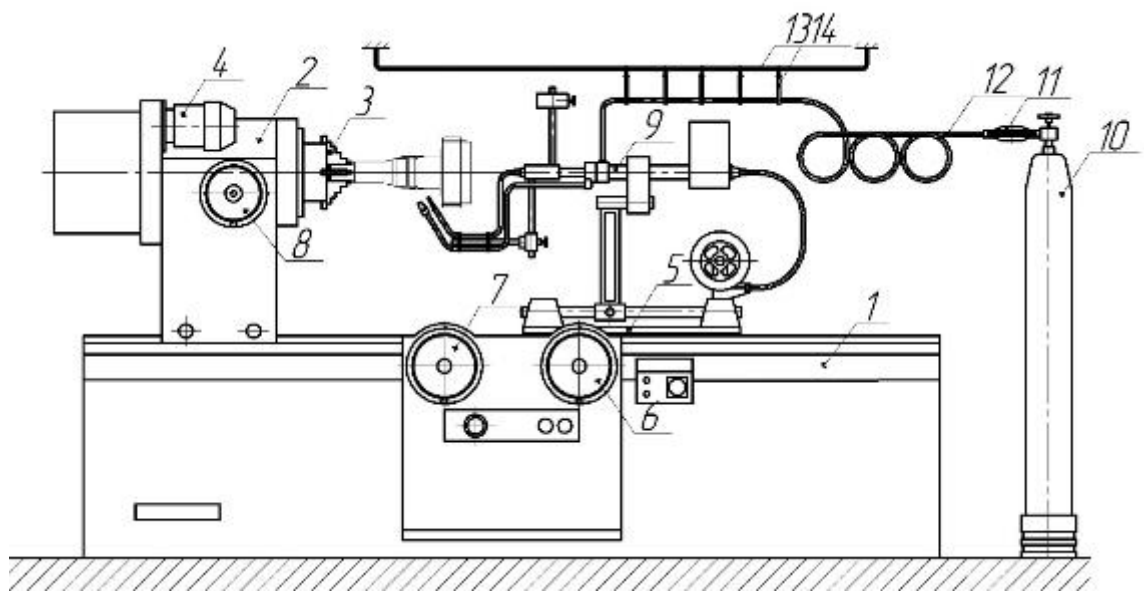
Установка для наплавлення циліндричних деталей.
